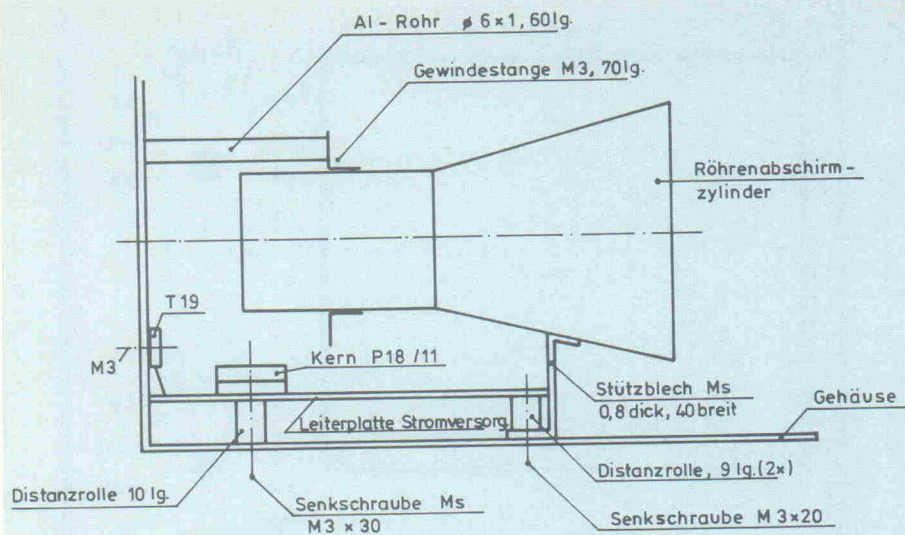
Der innere mechanische Aufbau des Oszilloskops.
